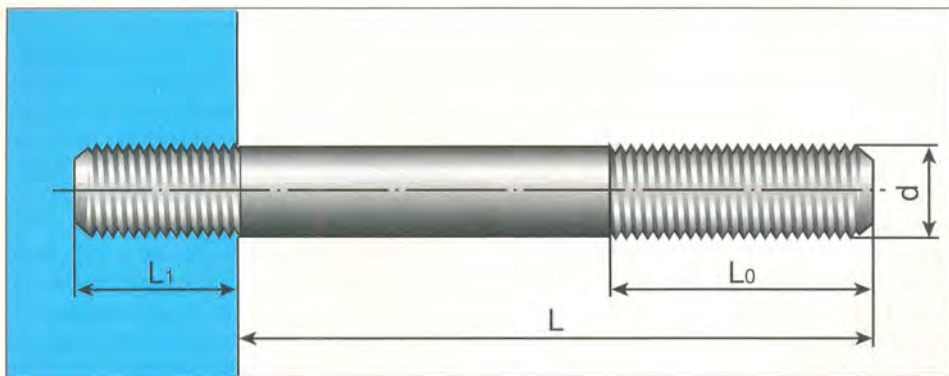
Основные размеры простой шпильки:  $L_1$  – длина резьбы ввертываемого конца;  $L$  – длина выступающей части;  $L_0$  – длина резьбы свободного конца;  $d$  – резьба шпильки.
